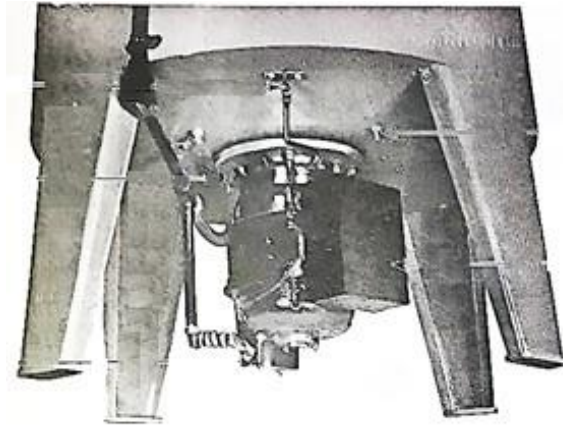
Instalación del motor en la parte inferior del horno [5].
